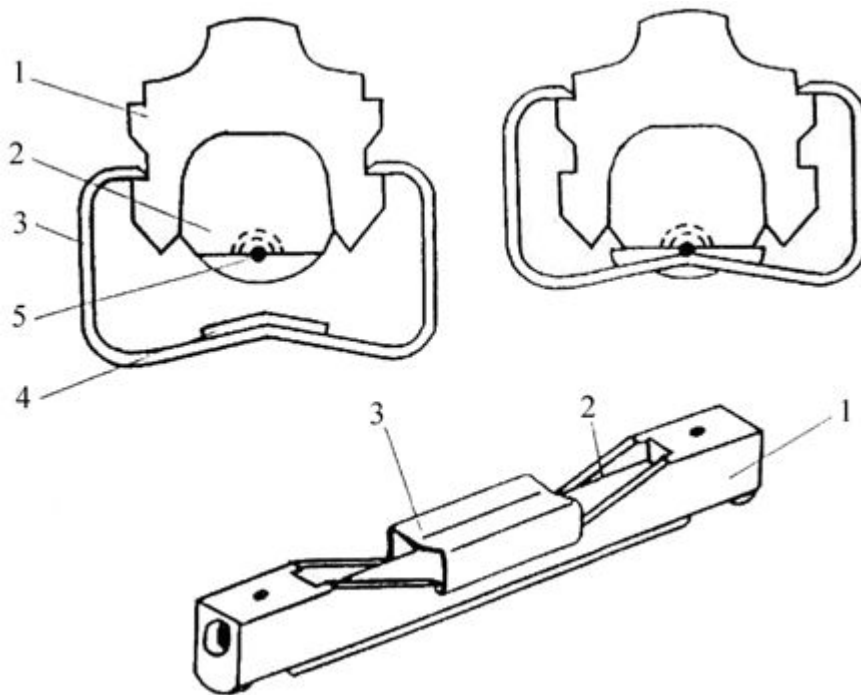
Механічний з'єднувач CSL LightSplice: 1 – прозорий пластиковий корпус, 2 – скляна капілярна трубка, 3 – металева пружина, 4 – тонкий шар еластичного матеріалу, 5 – процес з'єднання ОВ
